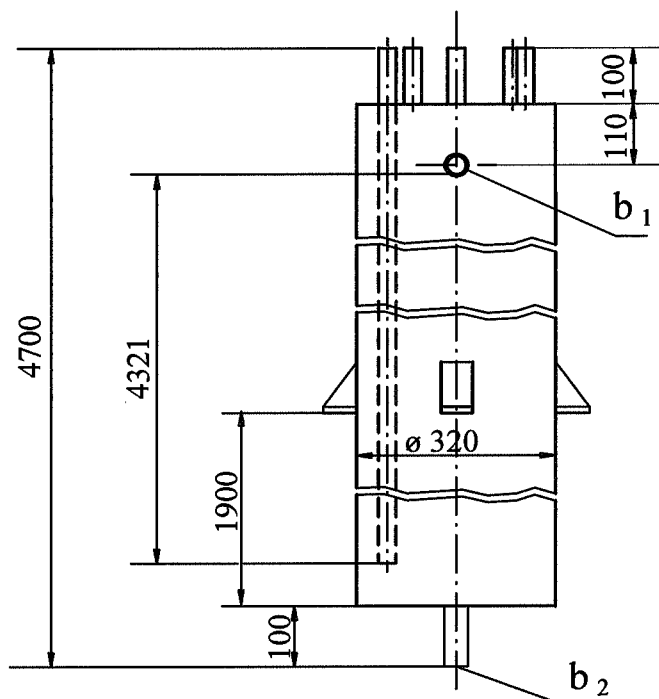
Габаритный чертеж бака-гидрозатора KPL10BV003, KPL31,32BV001
